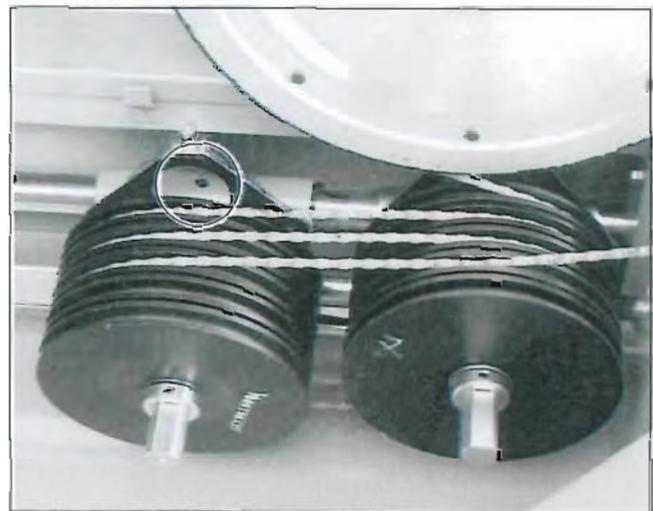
Направляющая накопителя, прессмасленка (смазочный ниппель)
